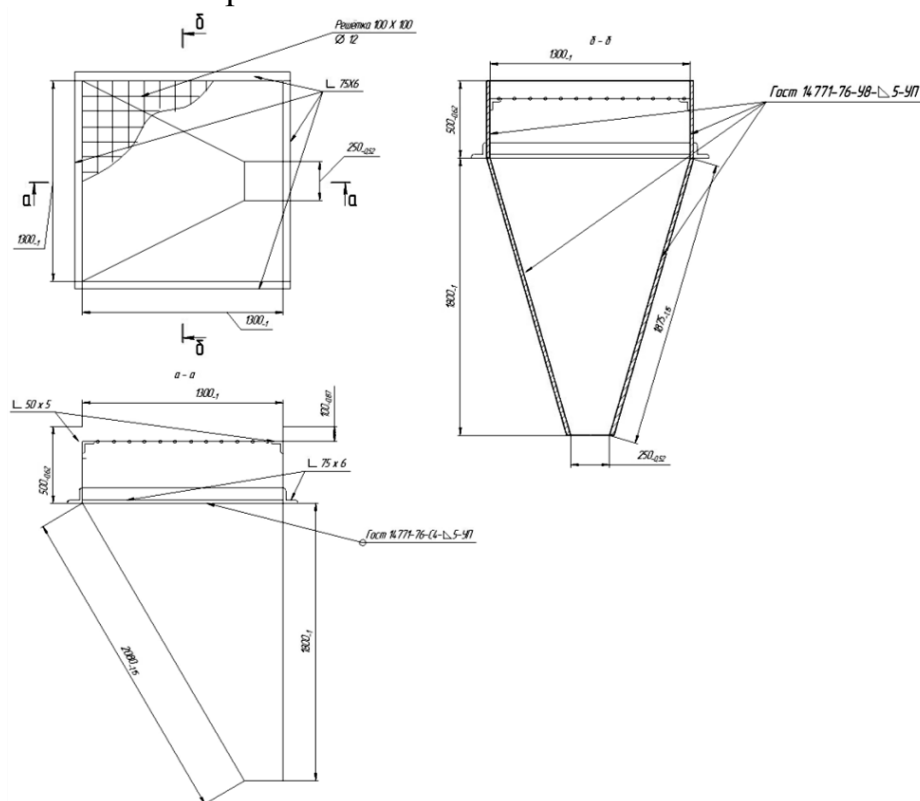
Чертеж бункера для сбора и дозирования коалиновой глины
